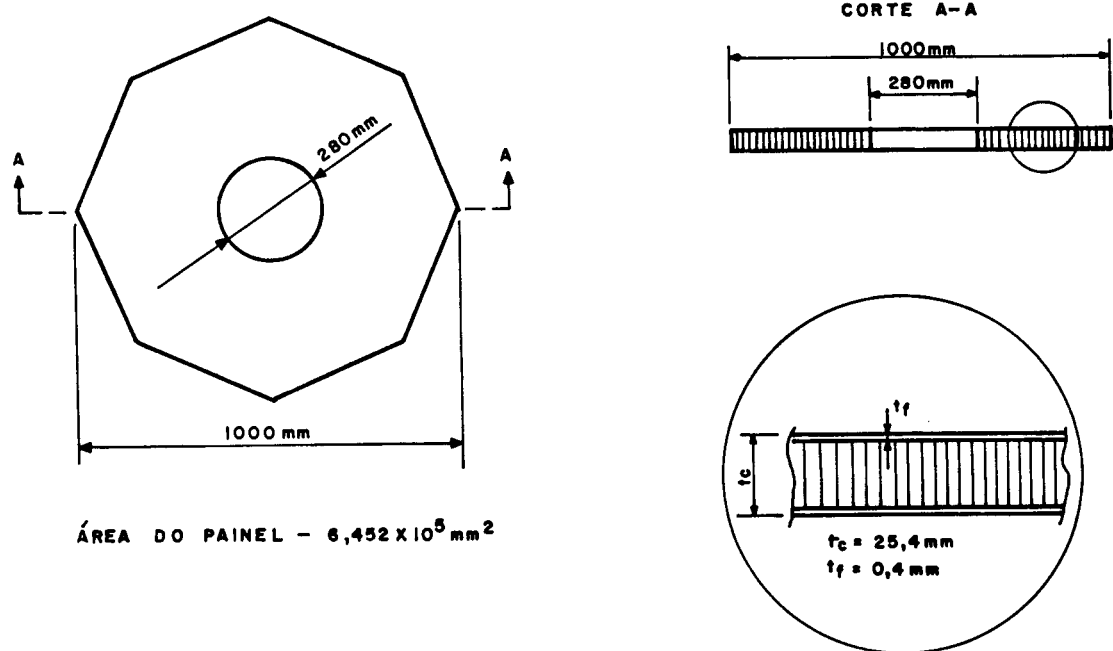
Dimensões do painel Porta-equipamentos.
